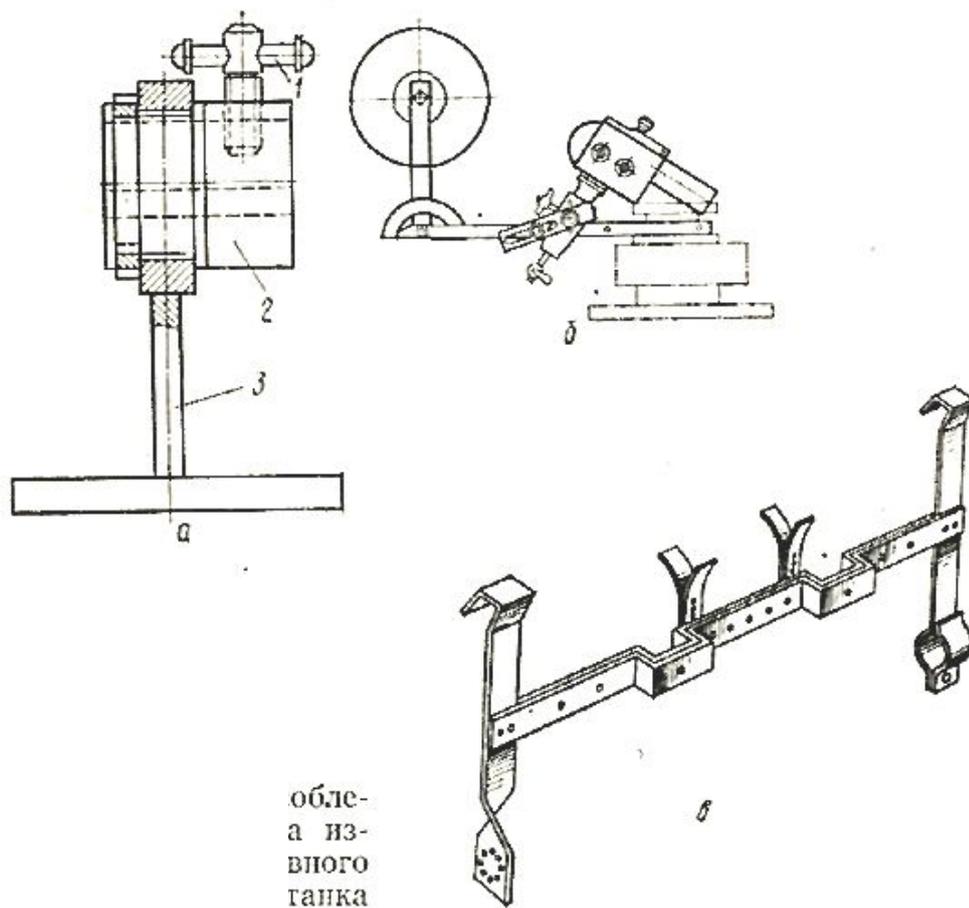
Приспособления для ремонта изношенного главного вала ткацкого станка.
